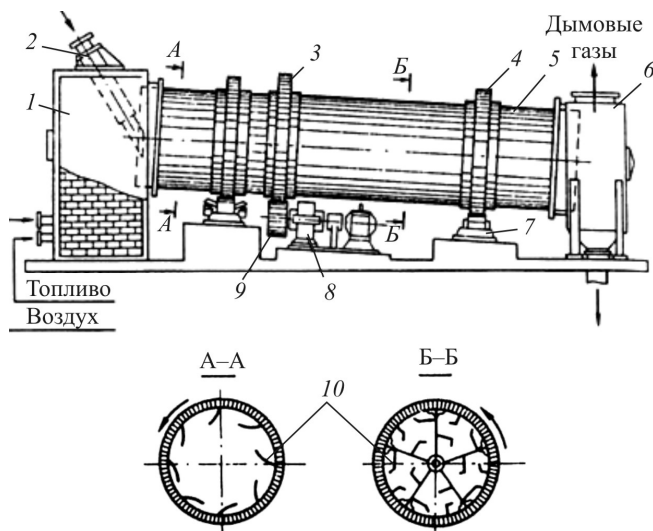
Барабанная сушилка: 1 – топка; 2 – загрузочная труба; 3 – венцовая зубчатая шестерня; 4 – бандаж; 5 – барабан; 6 – разгрузочная камера; 7 – опорные ролики; 8 – редуктор; 9 – шестерня; 10 – насадки
